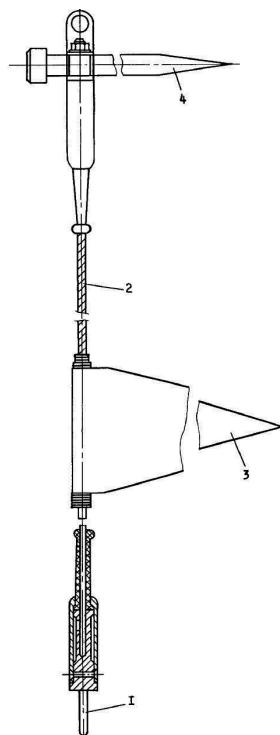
Приспособление для заземления самолетов Ту-204/214
